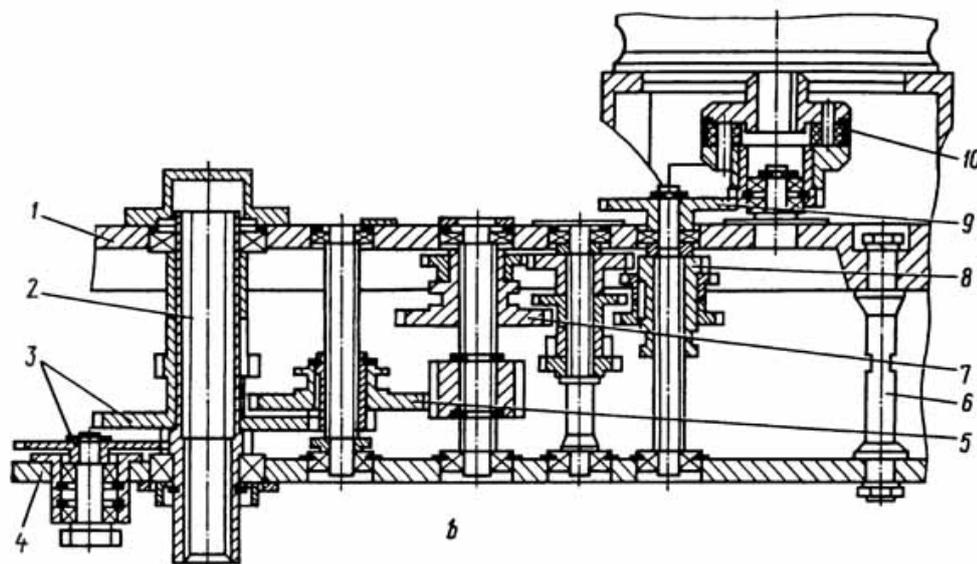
Коробка скоростей сверлильного станка 2Н135
